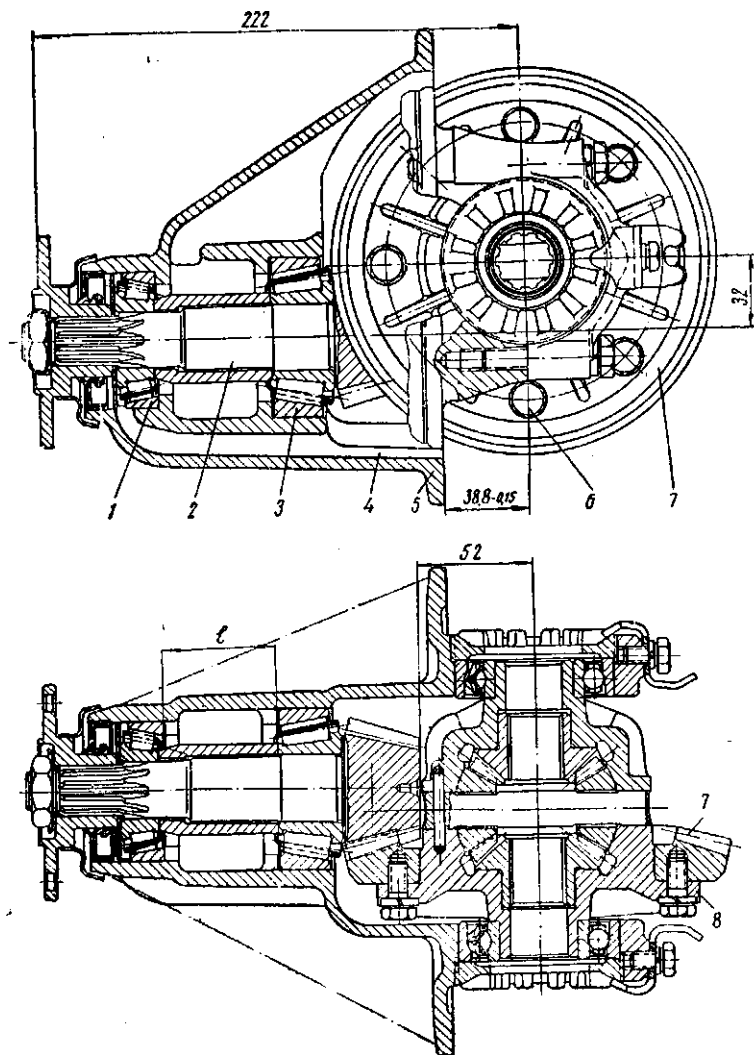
Главная передача коническими шестернями с гипоидным зацеплением:
